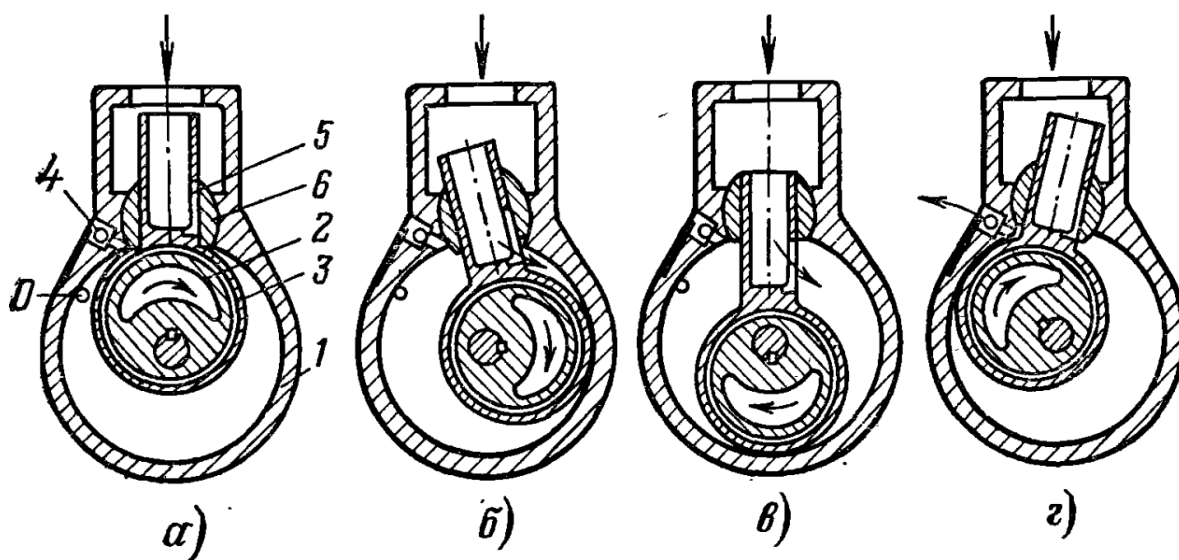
Принцип работы плунжерного (золотникового) насоса. 1 – цилиндрический корпус; 2 – эксцентрический ротор; 3 – плунжер; 4 – выхлопной клапан; 5 – окно; 6 – направляющая в шарнире [5, с. 96]
